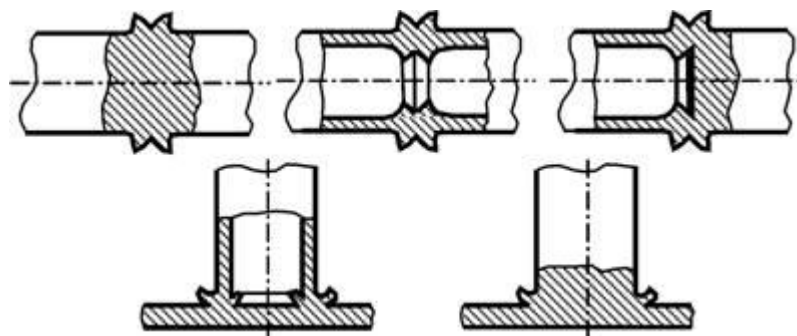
Типы сварных соединений, выполненных сваркой трением.
